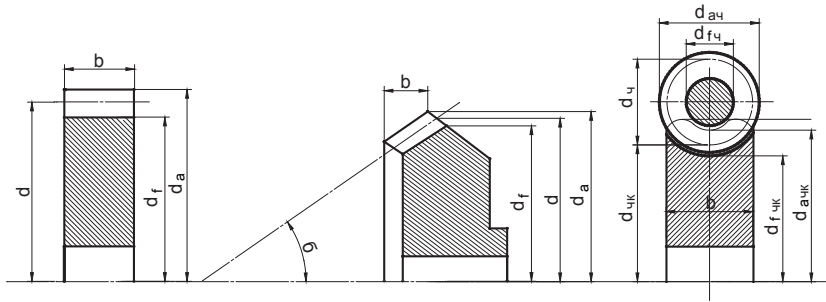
Зубчатые колеса: а – цилиндрическое; б – коническое; в – червячное
